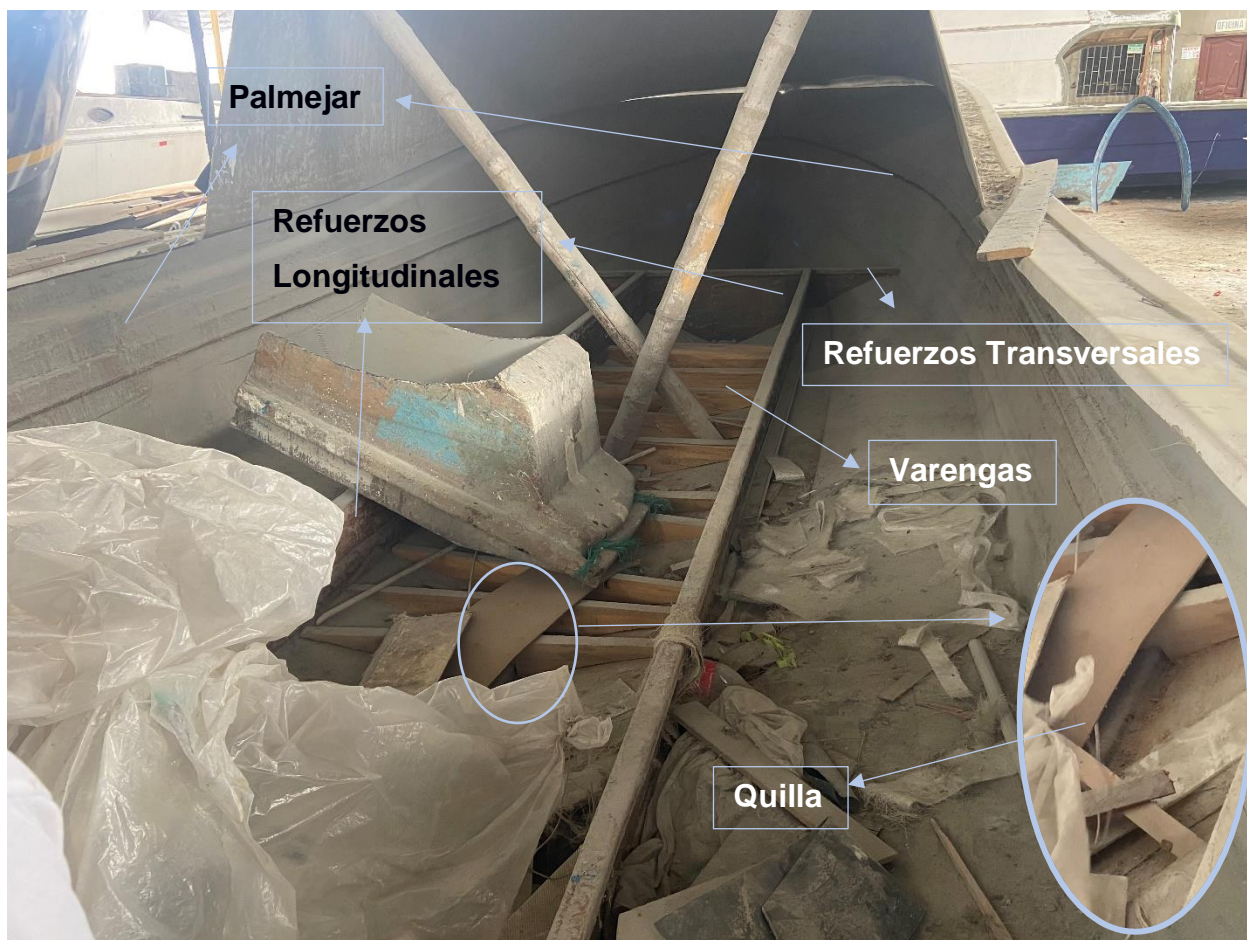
Refuerzos estructurales dentro de una embarcación para servicio similar a la lancha ANGY
